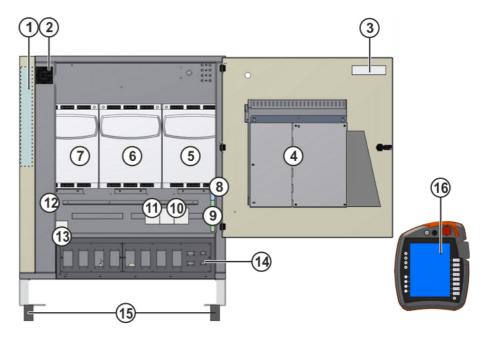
Vista general de la unidad de control del robot, vista frontal
